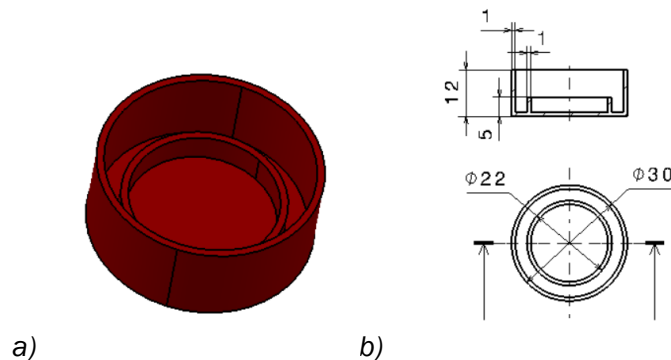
Tapón comercial. a) Vista isométrica; b) Dimensiones.
